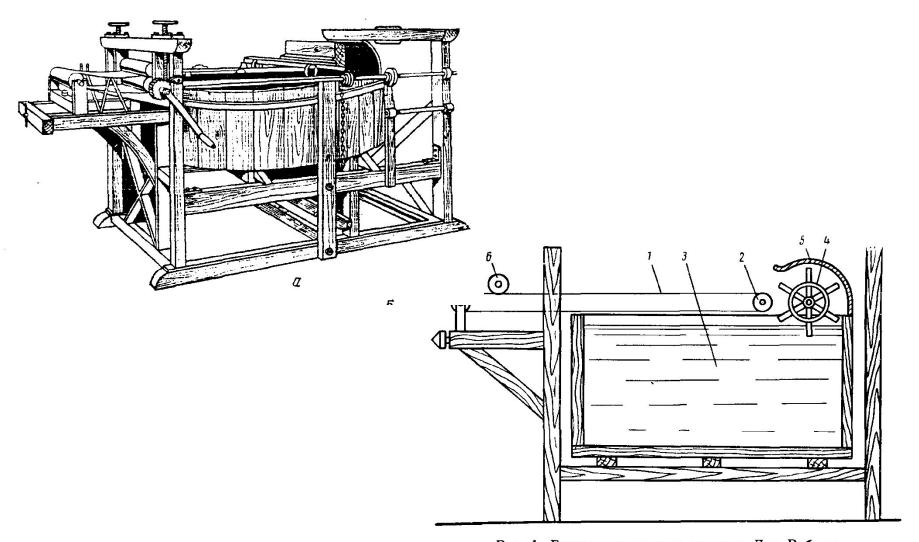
Бумагоделательная машина Луи Робера: 1- сетка; 2- валики; 3- черпальный бассейн; 4- черпальное колесо; 5- отражательный щит; 6- накат
